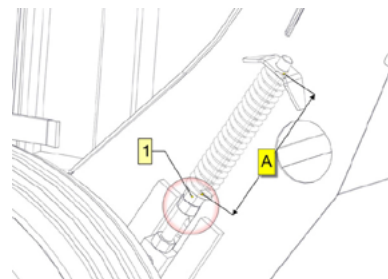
Регулировка натяжения цепно-пруткового транспортера
